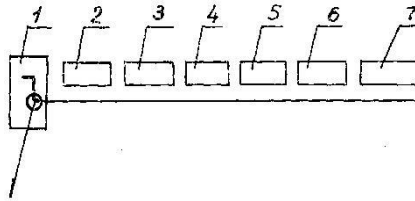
Структурная схема обозначения сварных швов на чертежах по ГОСТ 2.312–72
